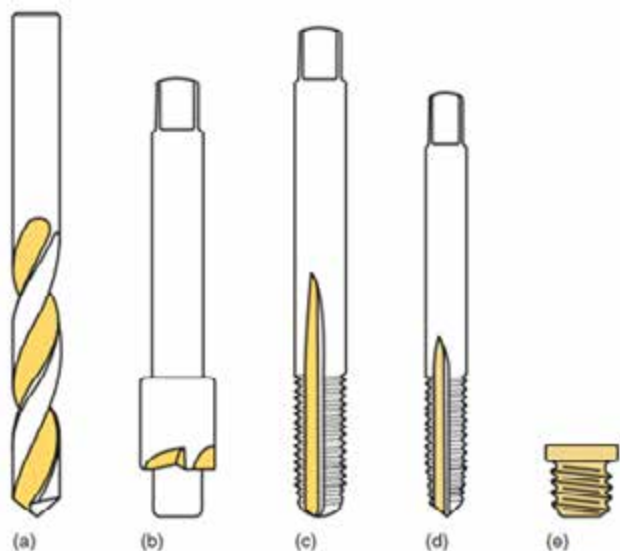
В комплект *Time-Set*<sup>®</sup> включены: сверло (a); торцевая фреза для выполнения углублений (b); специальный метчик для изготовления резьбы в ремонтируемом отверстии (c); метчик, используемый для установки вставки (d); твердо-втулочные вставки *Time-Set*<sup>®</sup> (e); источник:
